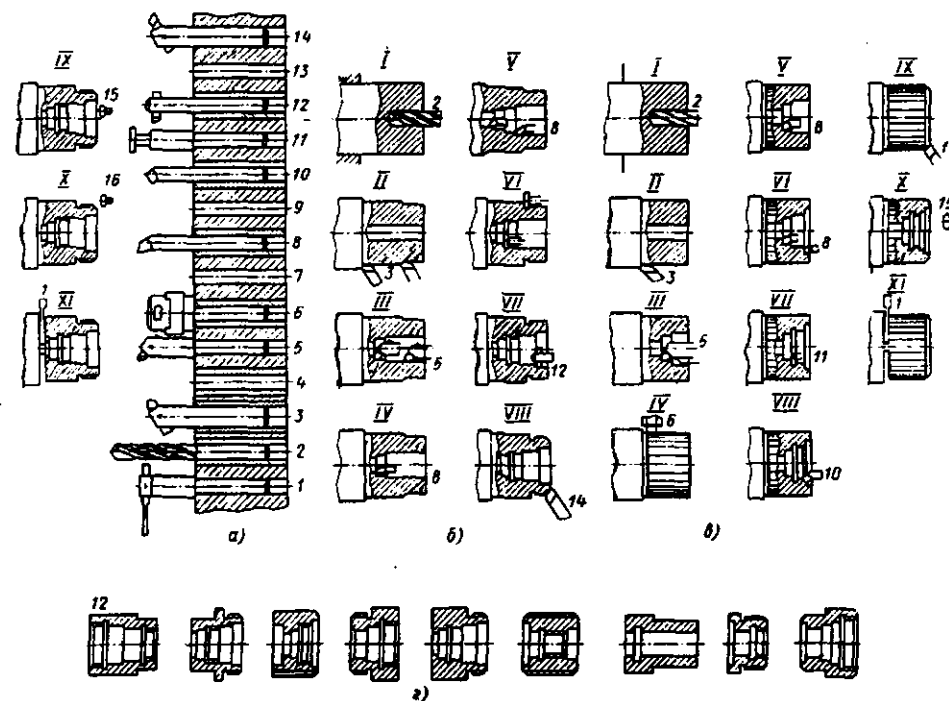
Схемы настройки револьверной головки для групповой обработки деталей: а – револьверная головка с комплектом инструмента; б, в – примеры выполняемых переходов обработки; г – типовые детали. I – XVI – переходы обработки; I – 16 – позиции инструментов в револьверной головке
